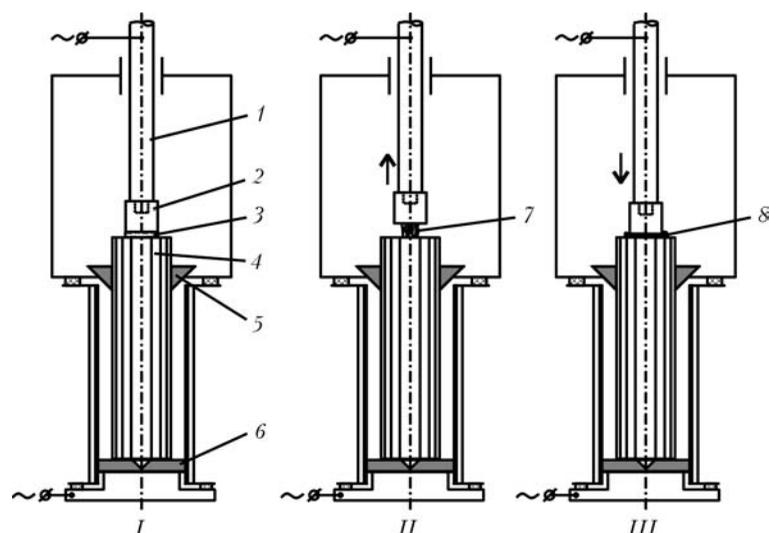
Схема приварки инвентарной головки к расходуемому электроду (I — нагрев соединяемых поверхностей проходящим током; II — оплавление поверхностей электрической дугой; III — осадка): 1 — шток вертикального перемещения электрода; 2 — инвентарная головка; 3 — токопроводящая прослойка; 4 — расходούμεый электрод; 5, 6 — соответственно центрирующие клинья и втулка; 7 — электрическая дуга; 8 — сварное соединение
